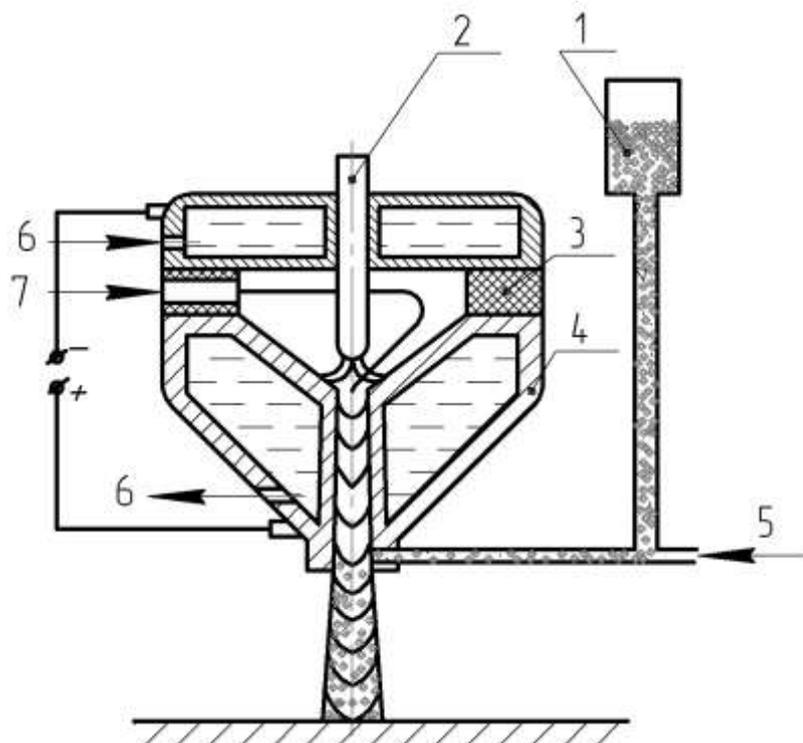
Схема плазменного напыления: 1 – порошковый дозатор; 2 – катод; 3 – изоляционная прокладка; 4 – анод (сопло); 5 – транспортирующий газ; 6 – охлаждающая вода; 7 – плазмообразующий газ
